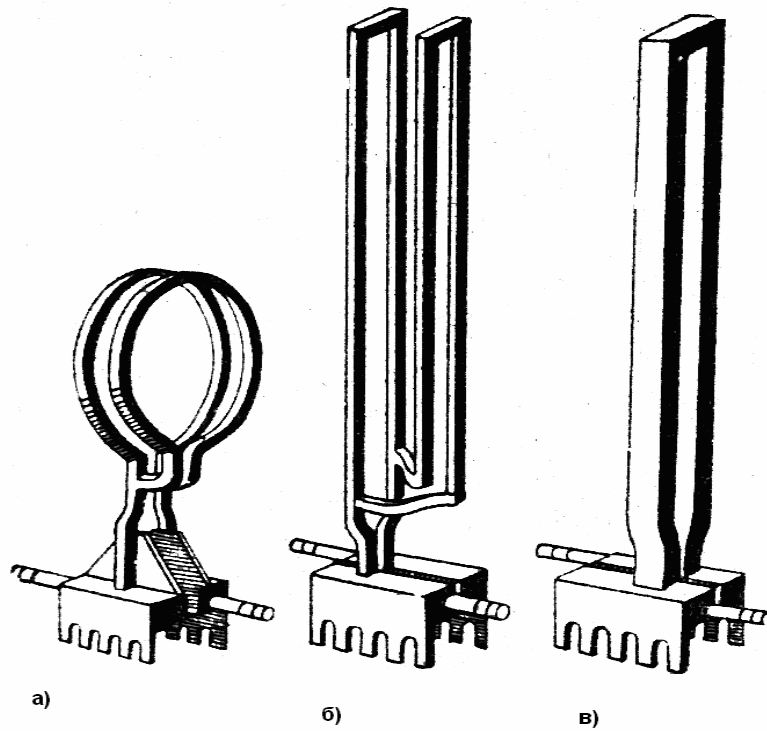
Індуктори для паяння твердосплавних дискових фрез [2]:
